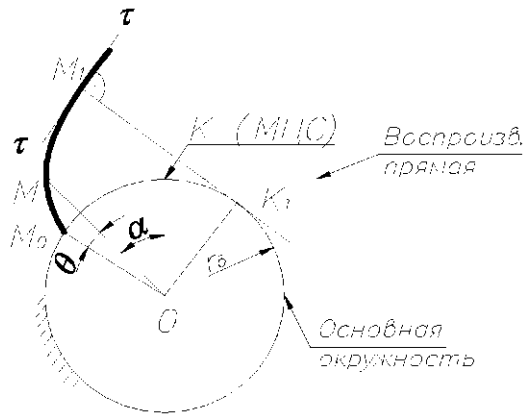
Схема образования боковой поверхности эвольвентного зуба
